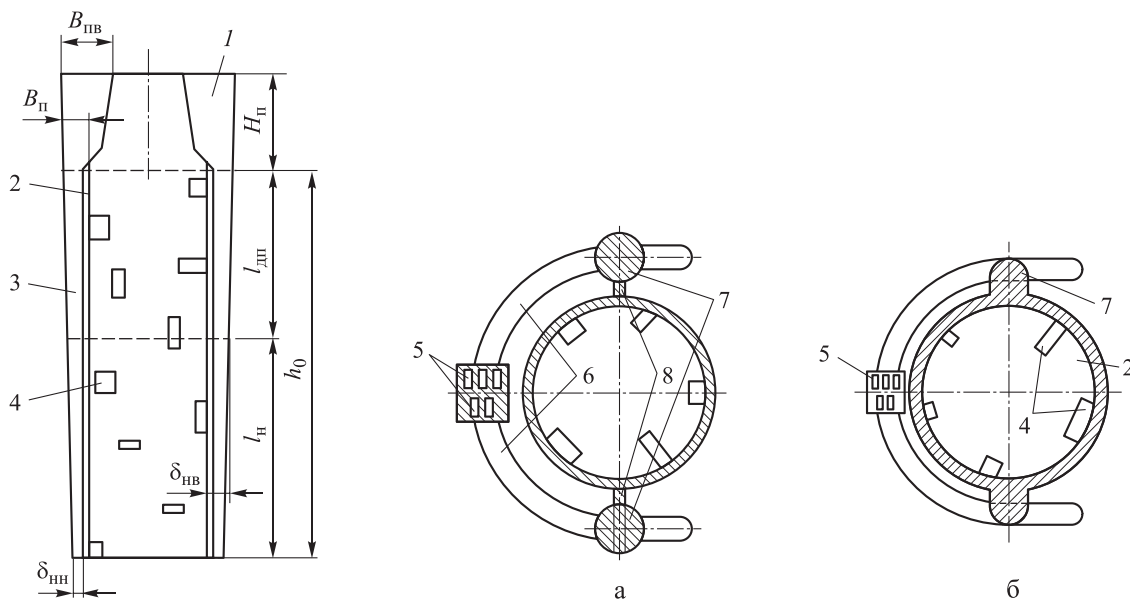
Схема корпусной тонкостенной отливки с вертикально-щелевой системой в случаях, когда вертикальная щель примыкает непосредственно к наружной стенке отливки (а) и когда роль вертикальной щели выполняет отливка (б):
